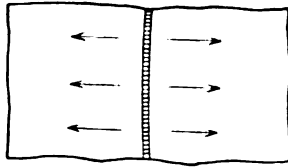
Spannungen quer zur Schweißnaht
